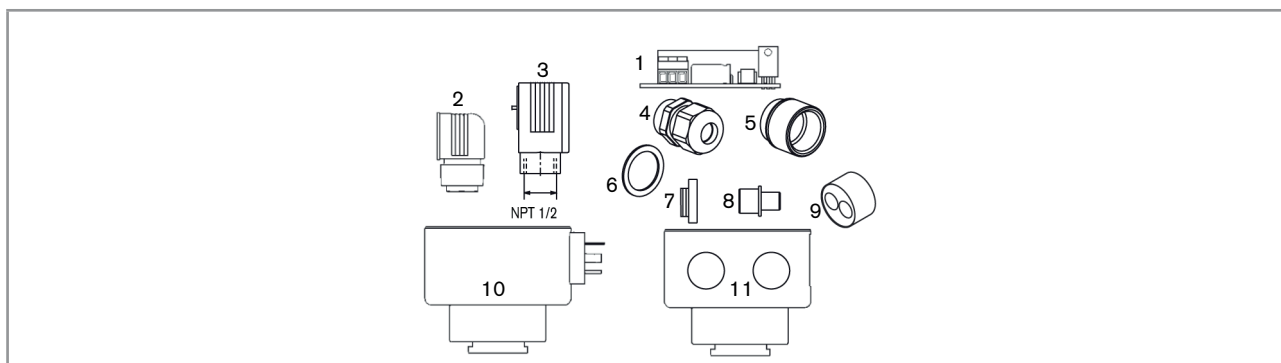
Explosionszeichnung der Ersatzteile, 8035 oder SE35
